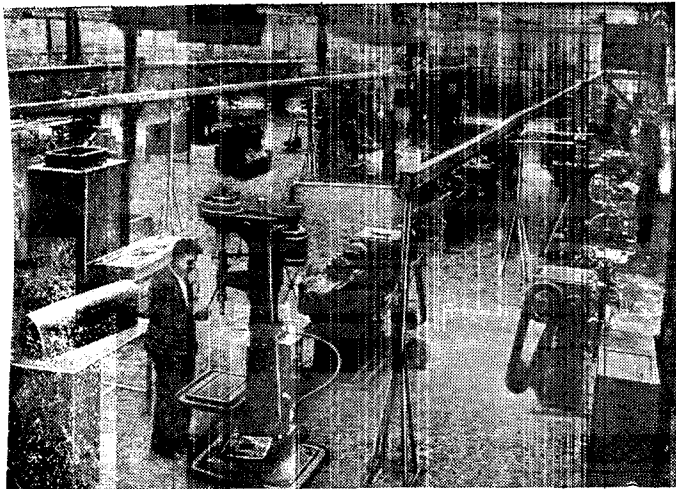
Общий вид цеха с распределительными шинными сборками в процессе монтажа
